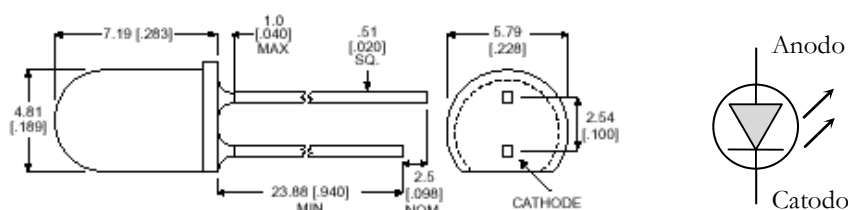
Dimensões do led – mm [pol.], e seu símbolo
